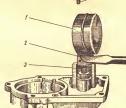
Регулировка уровня топлива в поплавковой камере полгибанием: рычажка поплавка: 1 — поплавок: 2 рычажек поплавка;
